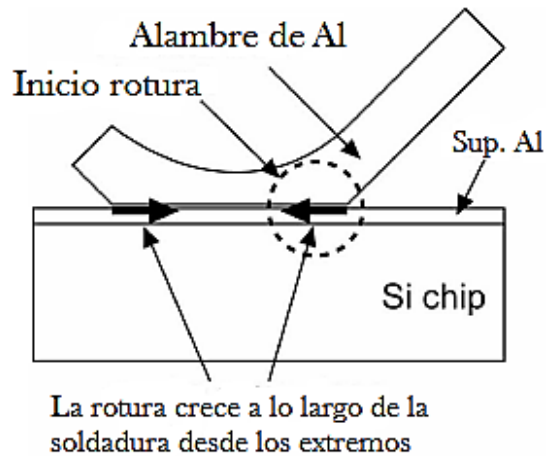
Despegue de alambres debido al crecimiento de grietas en la soldadura [27].
